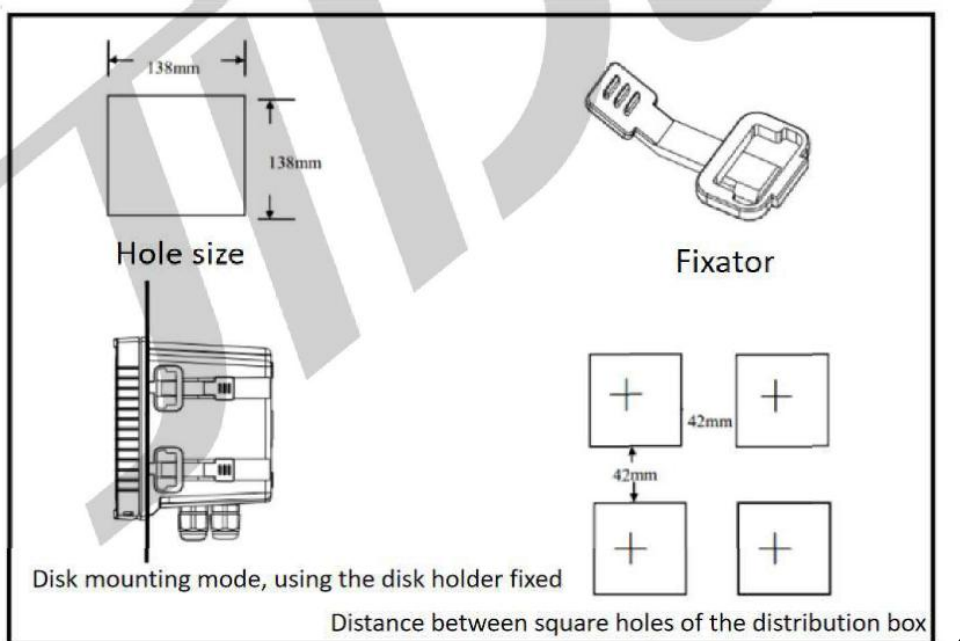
Eingebettete Installation des Controller-Panels
